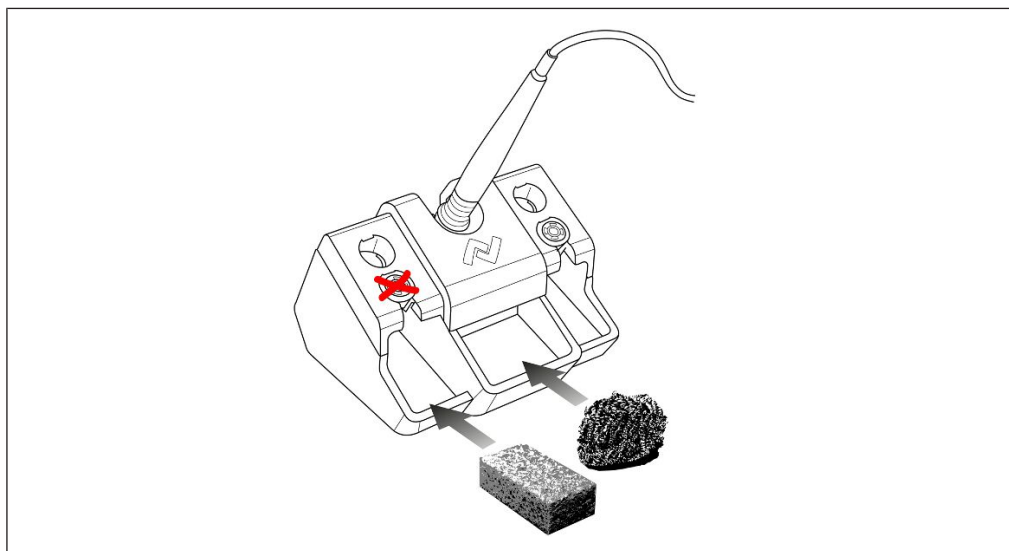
Bonne position de placement du fer à souder. Positionnement de l'éponge humidifiée et du nettoyeur à sec. Ne pas utiliser le placement avant du fer à souder, là où l'éponge est insérée !
